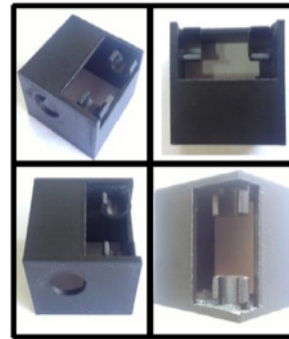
Pieza Resultante de impresión en Rapid Prototyping.
